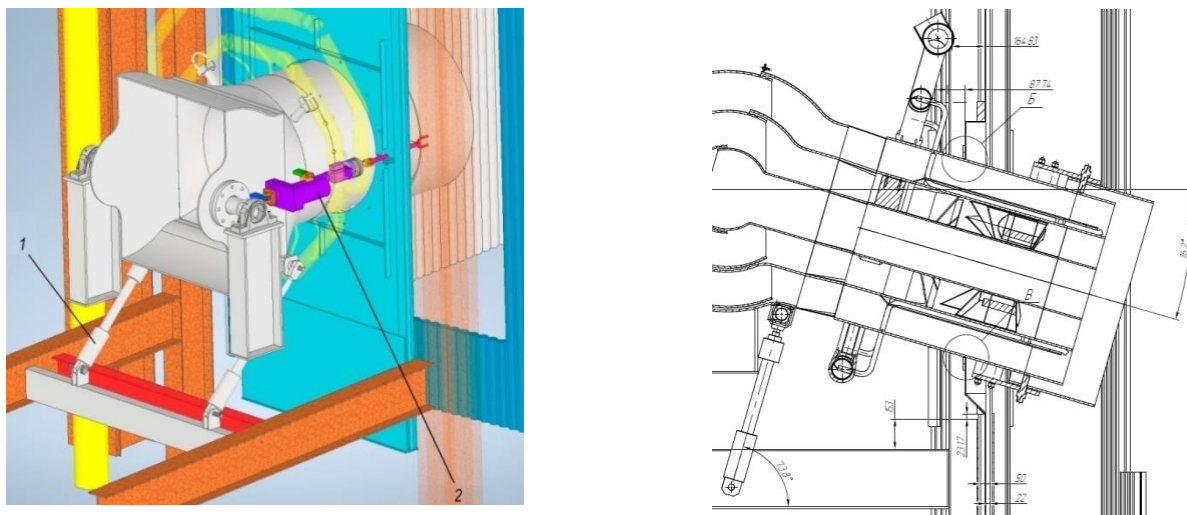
Схема установки гидроцилиндров для реализации вертикального поворота: а) исходная конструкция; б) усовершенствованный вариант после первичного опробования (1 – гидроцилиндр; 2 – МЭП)
